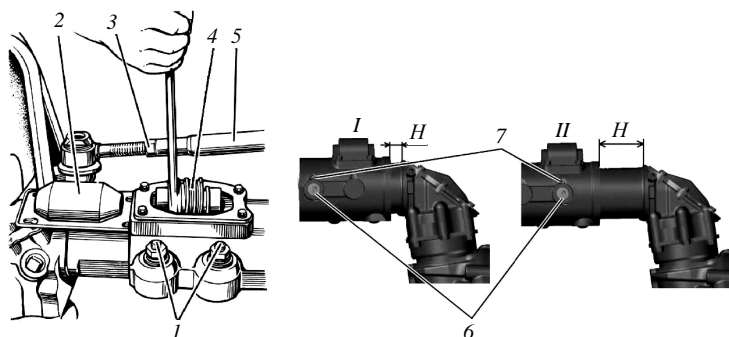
Схема изменения колеи передних колес трактора с коническими колесными редукторами: 1 – клинья; 2 – крышка регулировочного винта; 3 – гайка; 4 – регулировочный винт; 5 – труба рулевой тяги; 6 – фиксирующий палец; 7 – шплинт
